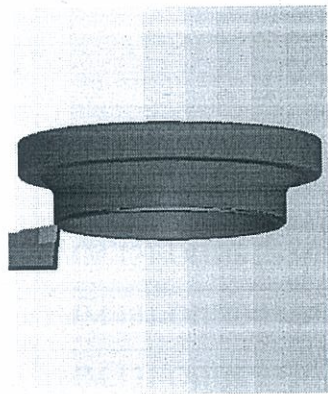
Обробка задньої циліндричної і конічної поверхні
